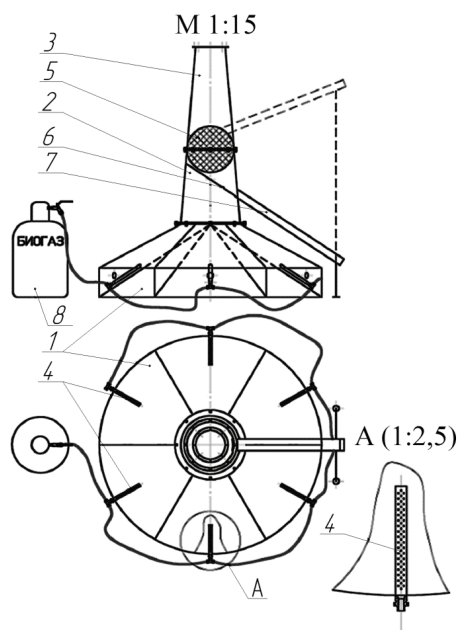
Установка сушки в «кипящем» слое: 1 – сопловой блок; 2 – нижний конус; 3 – верхний конус; 4 – горелка; 5 – газораспределительная решетка; 6 – устройство загрузки материала; 7 – устройство выгрузки материала; 8 – баллон с биогазом (попутным газом)
